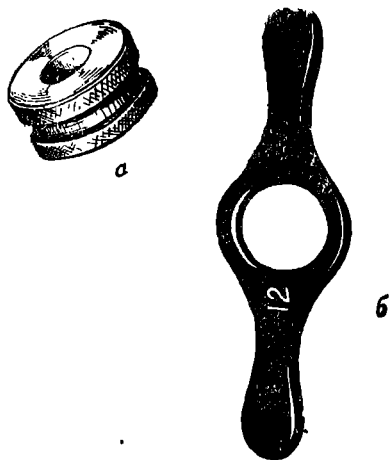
Калибровочные кольца для металлических (а) и папковых (б) гильз
